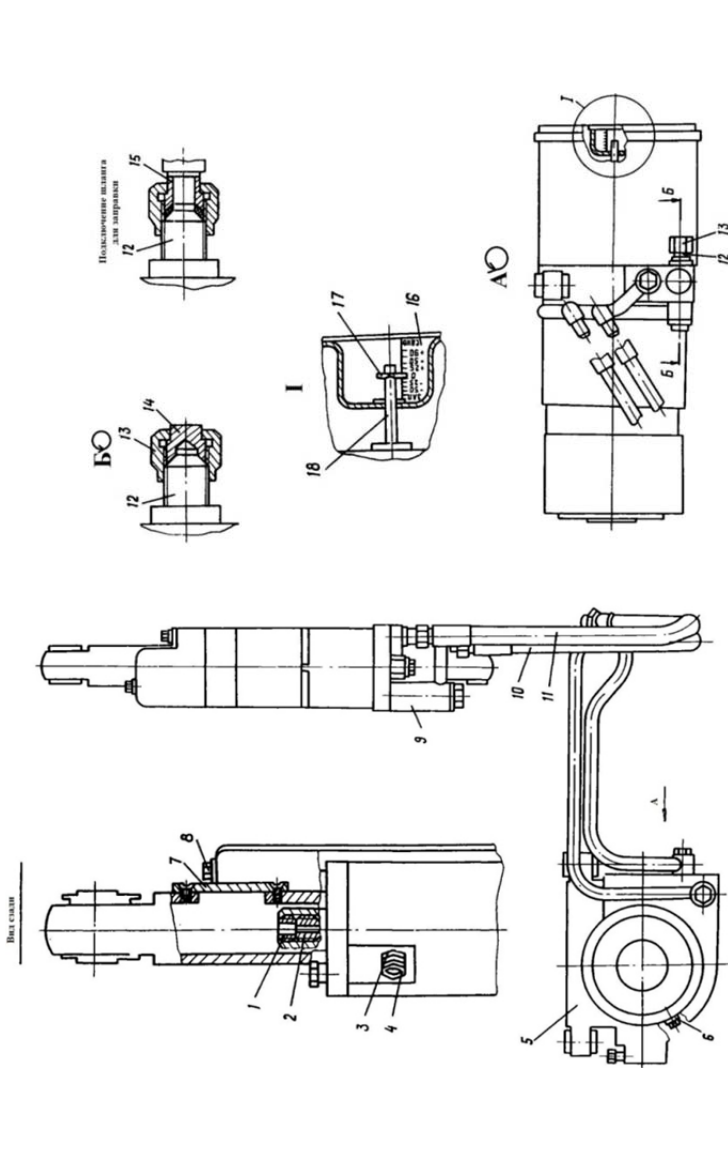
Выпуск воздуха из питающей установки и исполнительного цилиндра:
